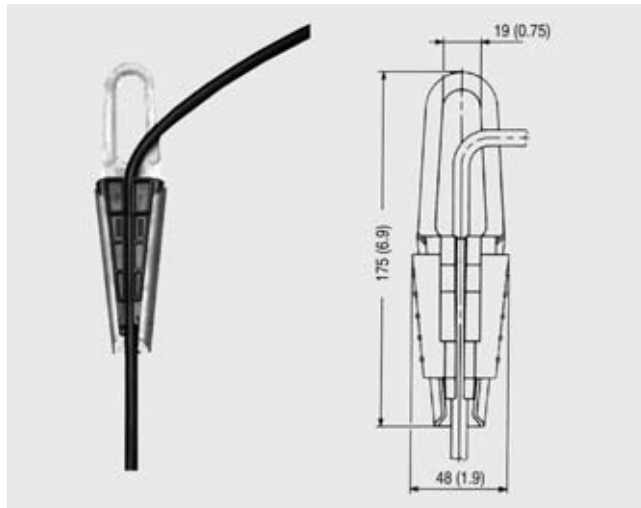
Staffa di fissaggio 7MF1570-8AB, dimensioni in mm (inch)
